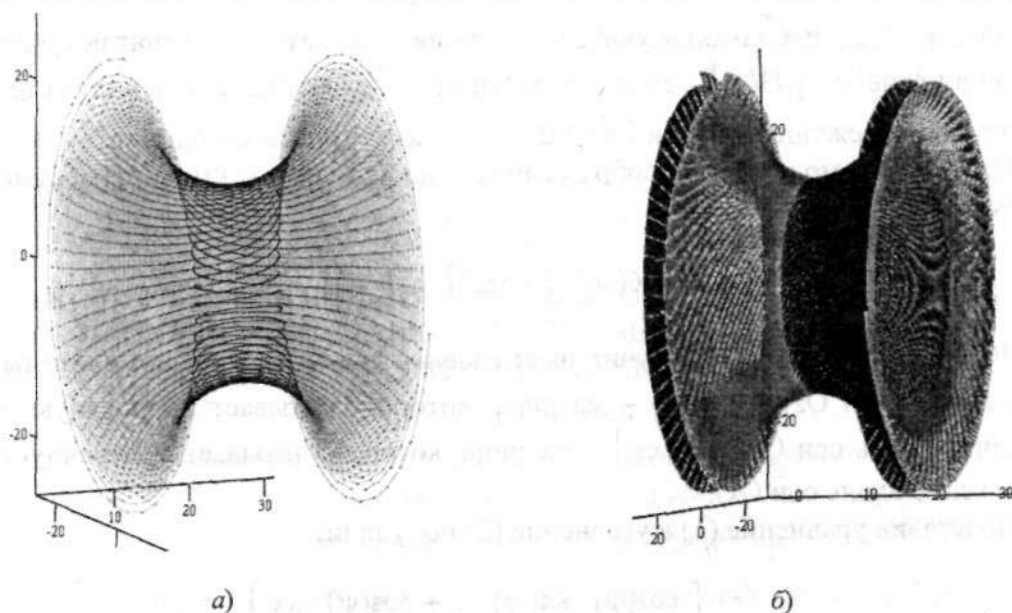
Траектория движения точки режущей кромки резца (а); топография обработанной поверхности (б)
